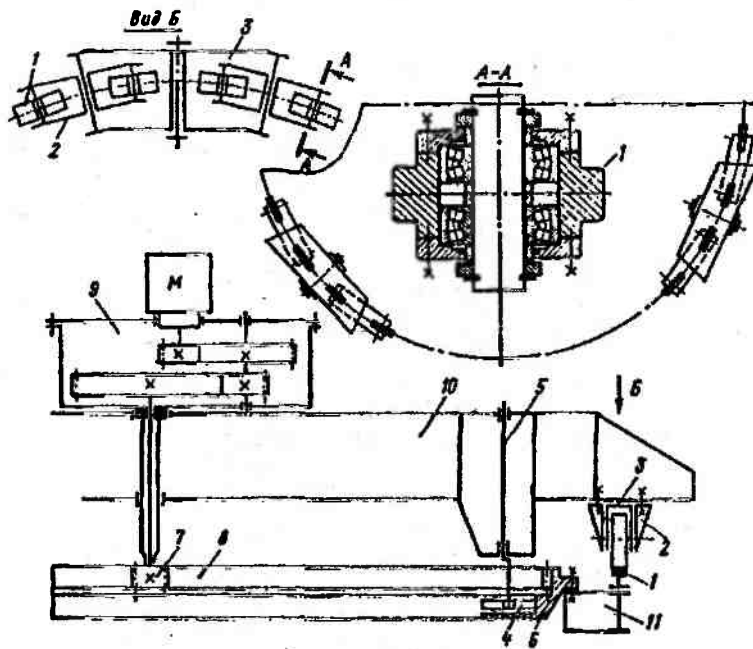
Опорно-поворотное устройство многоковшового экскаватора с катками, закрепленными на осях балансиров
